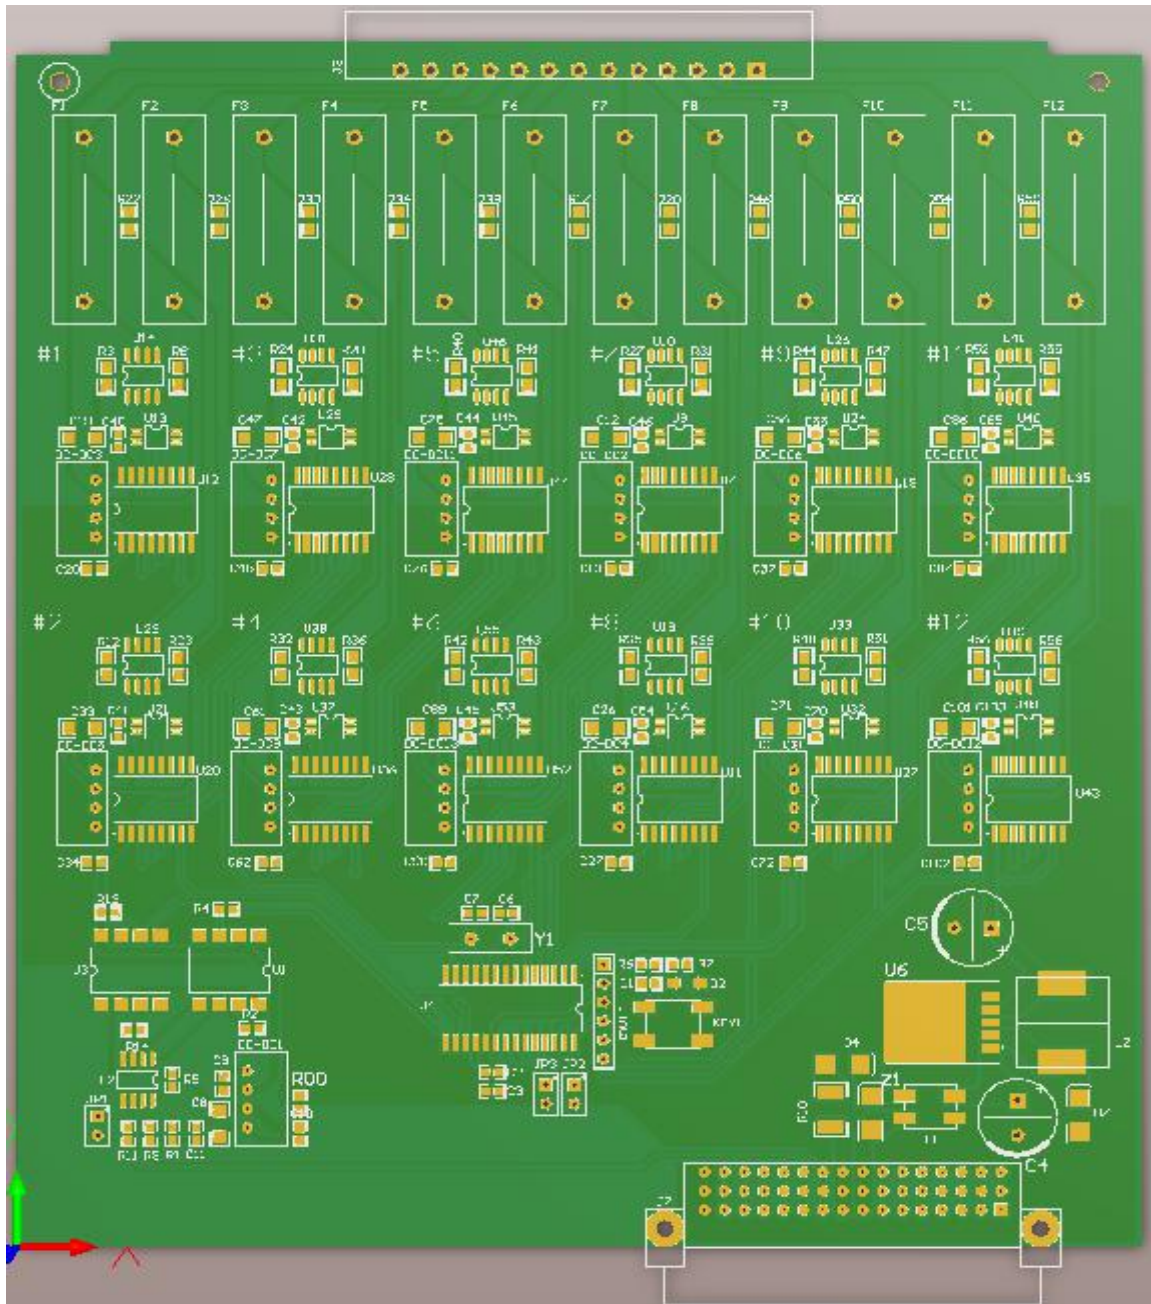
十二路电压模拟 PCB 图纸 (Print circuit board, PCB)
